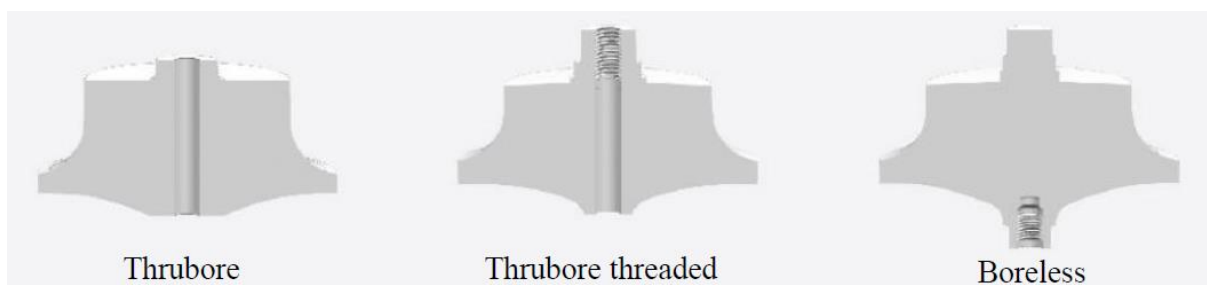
Boreless a Thrubore riešenie pripojenia kompresorového kolesa[3]
